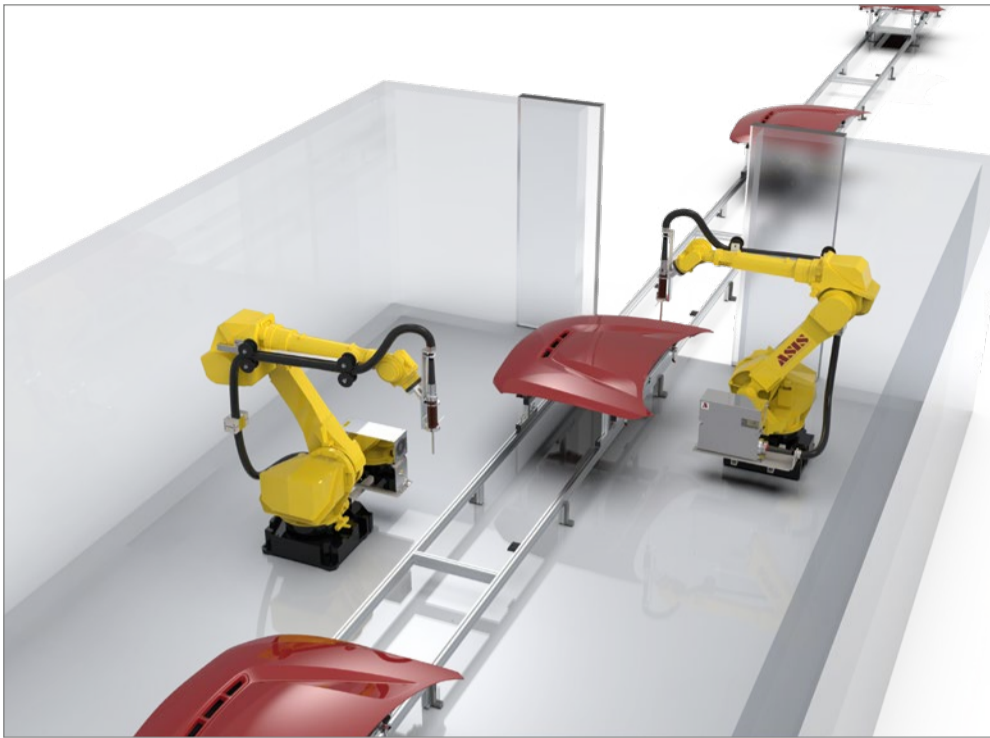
Die robotergesteuerte Härting macht auch dreidimensionale Formteile für die Härting per Elektronenstrahl zugänglich.
